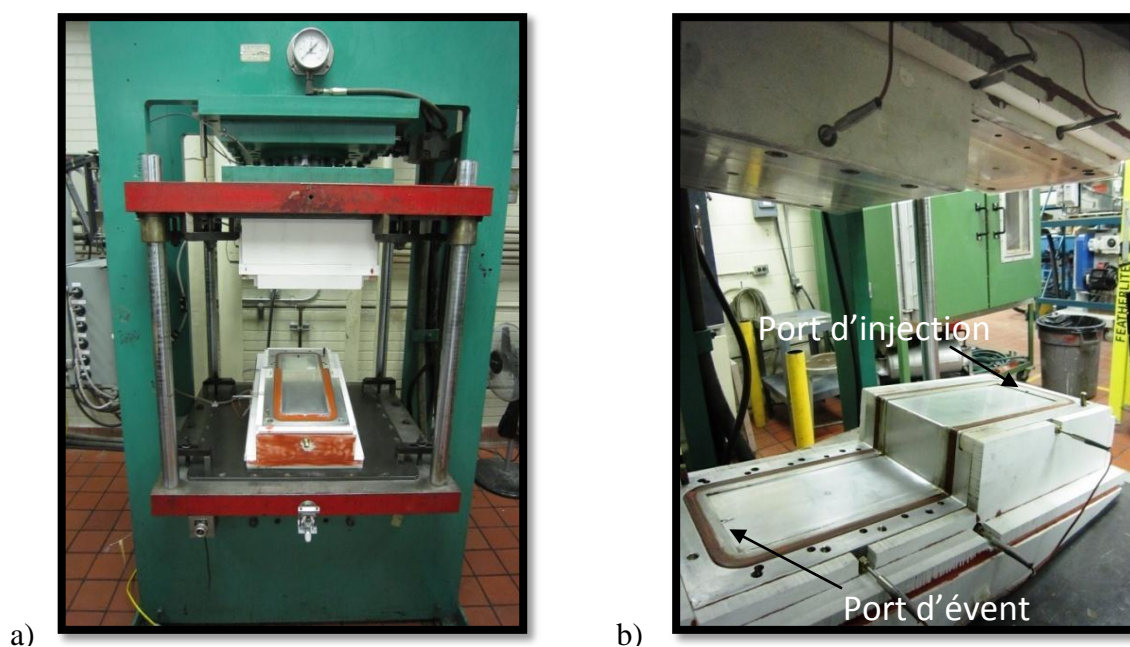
Photographies du moule : a) vue d'ensemble du moule dans la presse ; b) vue rapprochée du moule.
